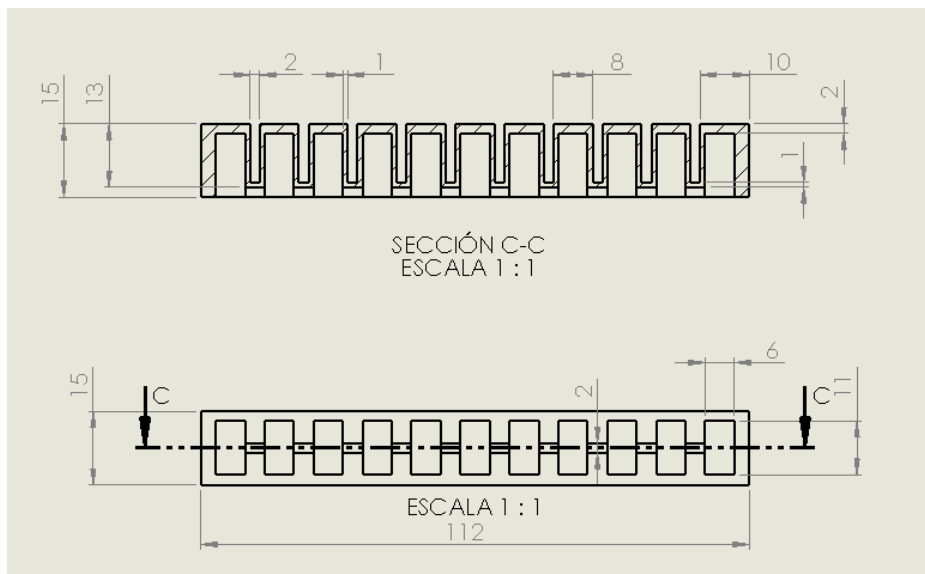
Molde de la capa inferior inextensible del actuador.
